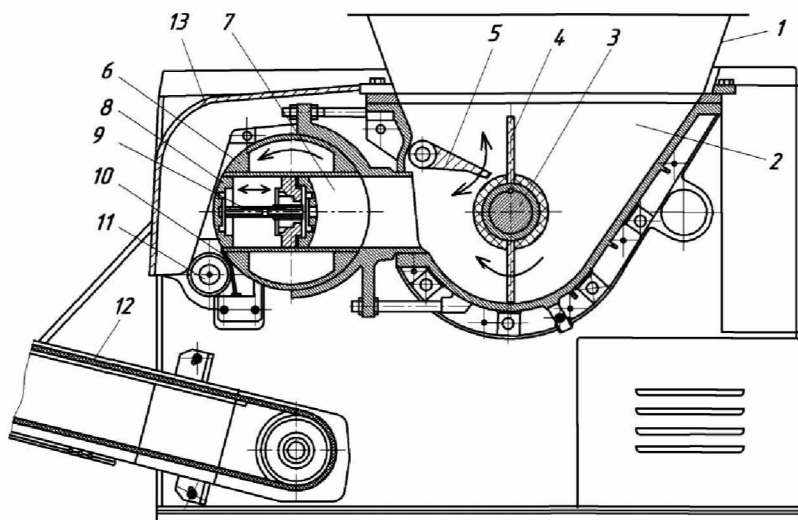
Тістоподільна машина А2-ХТН: 1 – приймальна воронка; 2 – робоча тістова камера; 3 – вал; 4 – лопать; 5 – заслінка; 6 – подільна головка; 7 – мірна камера; 8 – плаваючий поршень; 9 – втулка з різьбою; 10 – ніж; 11 – валок; 12 – стрічковий транспортер; 13 – захистний кожух.
